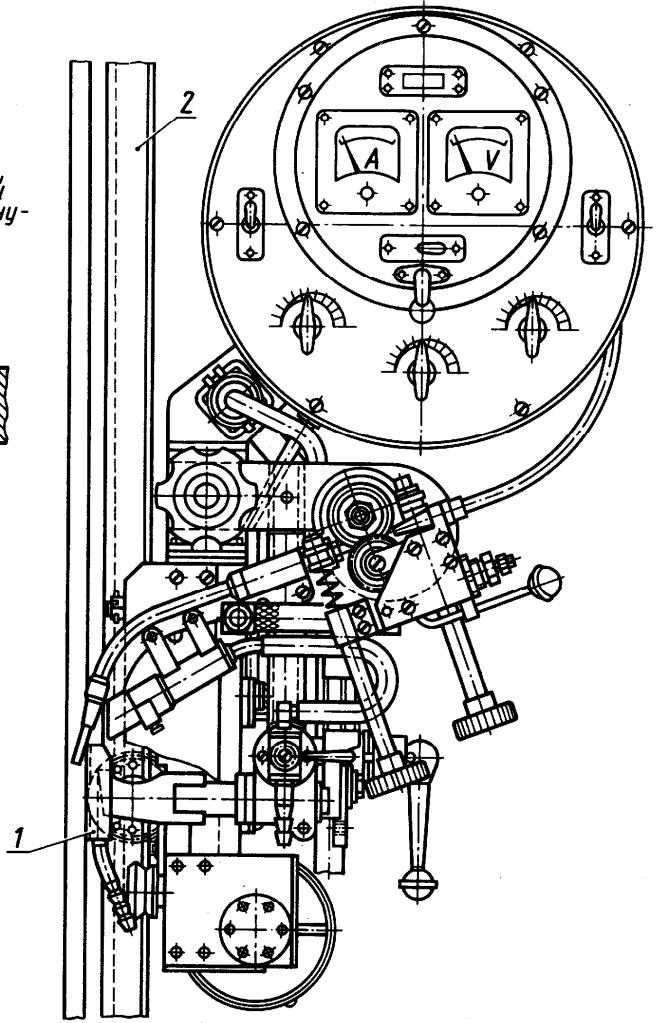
Сварочный автомат для сварки швов с принудительным формованием
